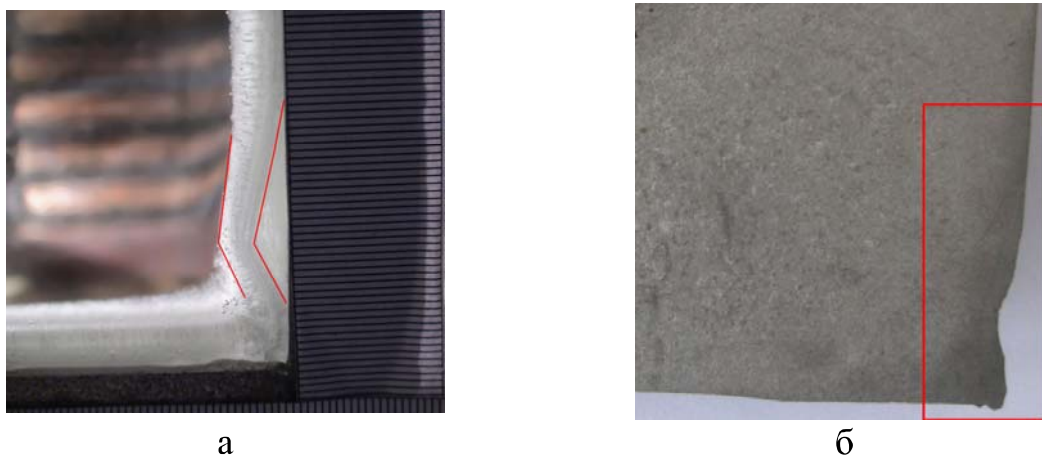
Фотография корочки модельного вещества в месте деформации при наложении на нее сжимающего воздействия (а) и профиля темплета непрерывнолитой сортовой заготовки сечением 125 мм (б).
